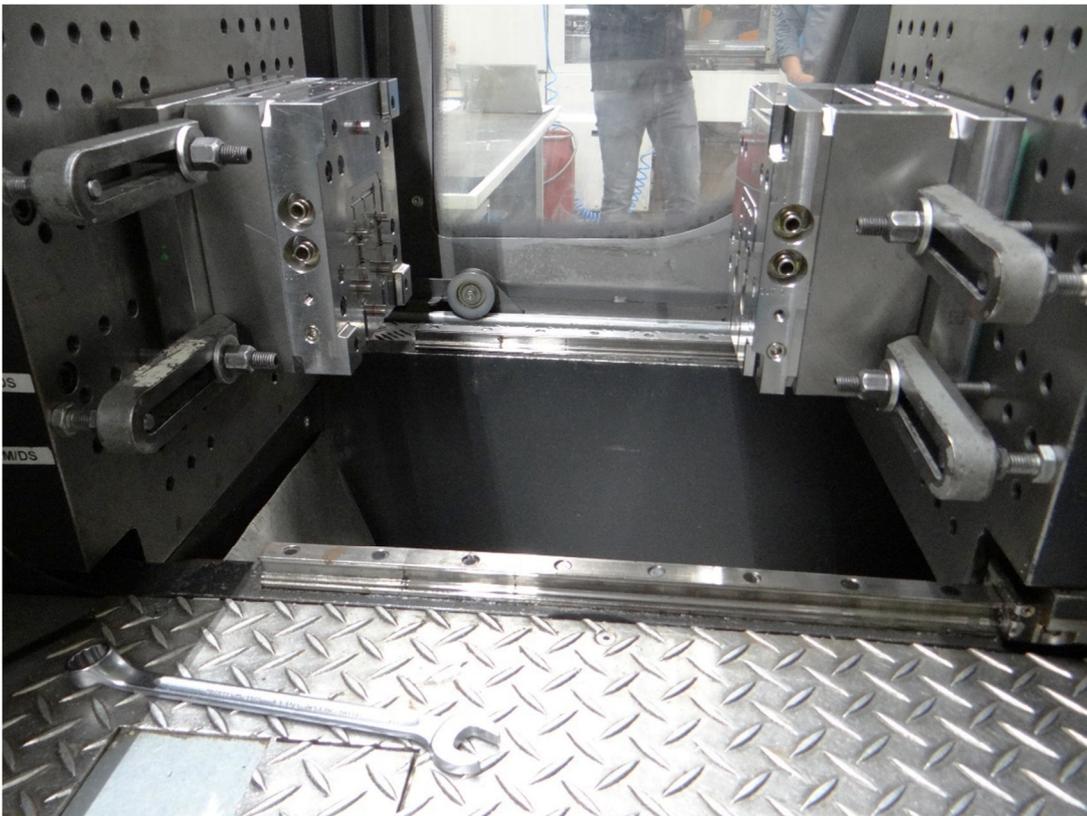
Werkzeug im aufgefahrenen Zustand
